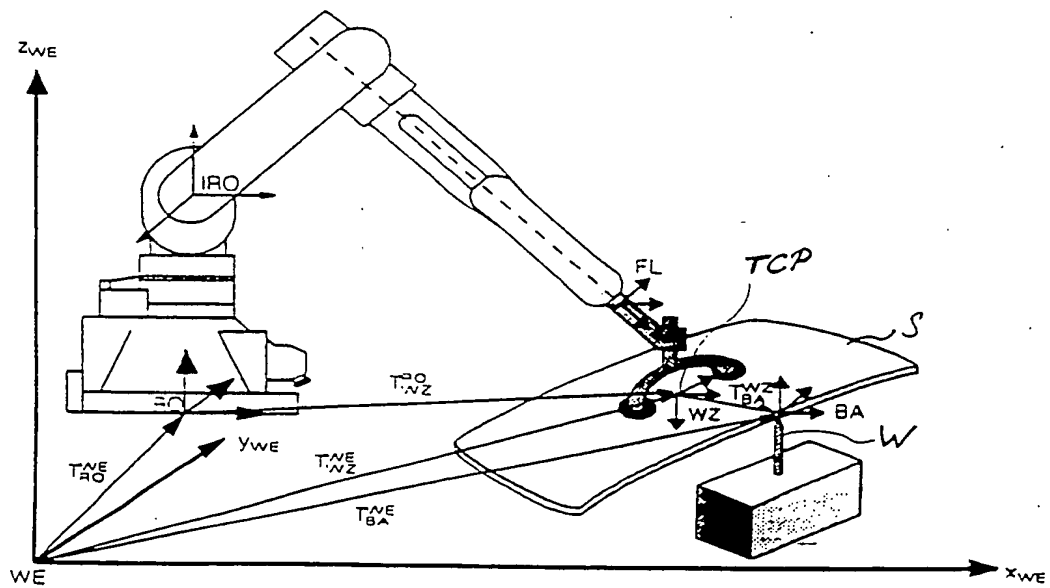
Führung des Werkstücks über ein ortsfestes Werkzeug
